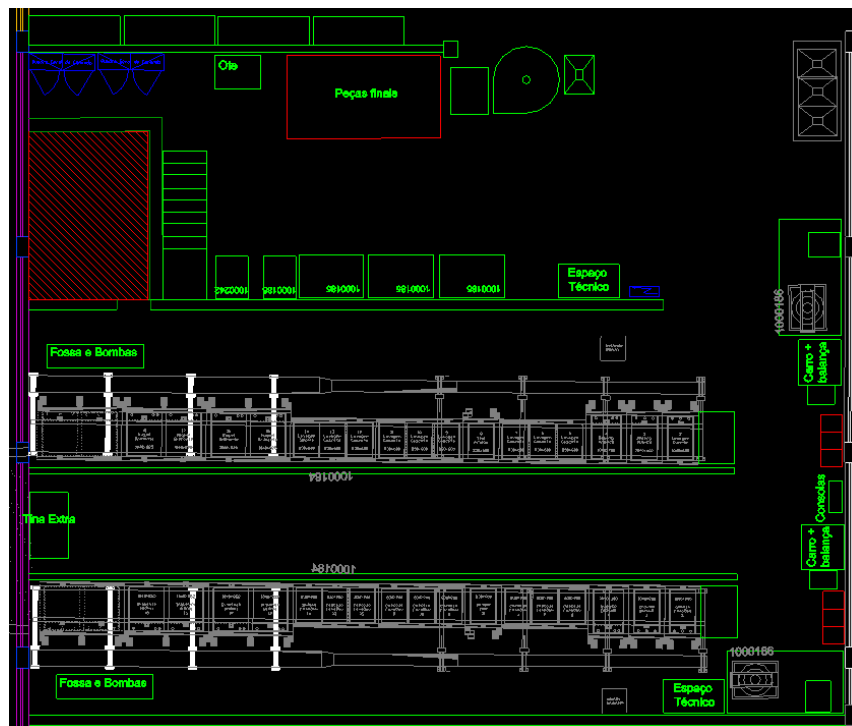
Layout futuro proposto para o aumento da unidade fabril da SRAMPORT.
